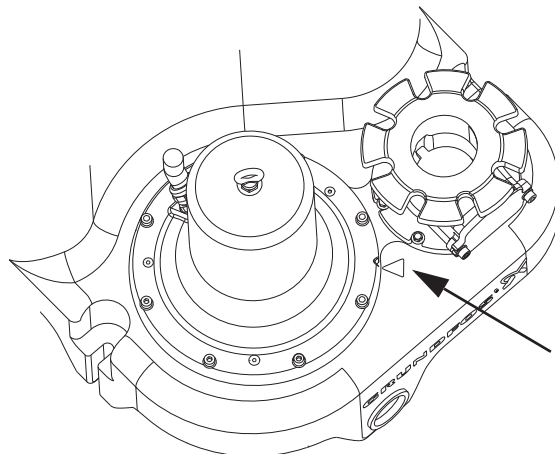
Метки совмещения на резервуаре и фланце насоса
